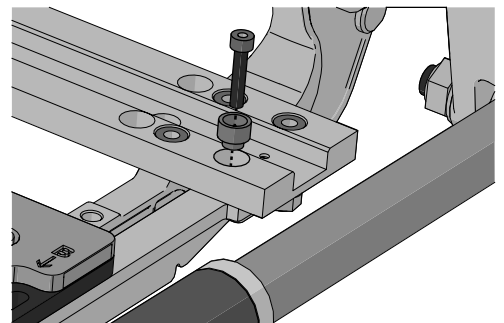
Die M4x20-Schraube durch die Buchse befestigen.
